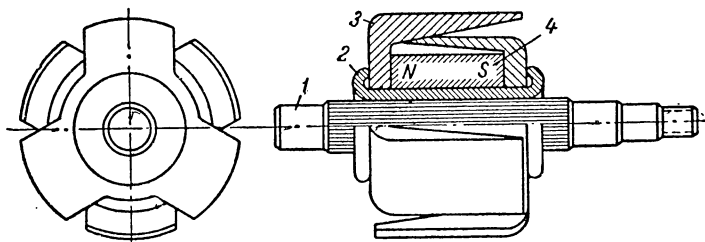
Ротор с «когтеобразными» полюсами: 1 — вал; 2 — немагнитная втулка; 3 — полюс; 4 — цилиндрический магнит
